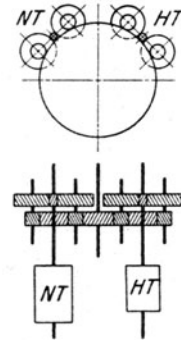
Aufnahme des Schubes durch die axiale Komponente des Zahndruckes.
